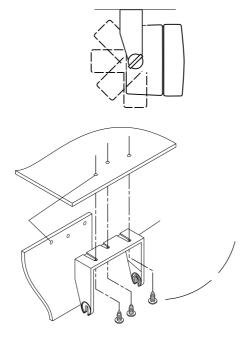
Montage des Lautsprechers unter dem Armaturenbrett
